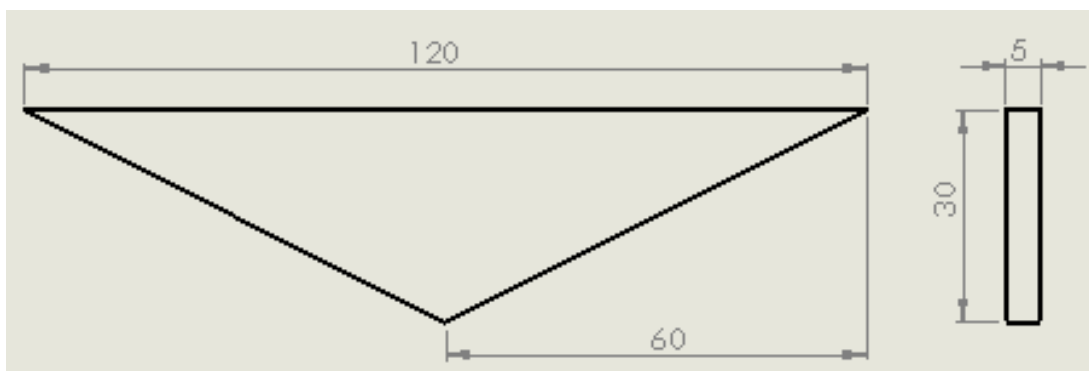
Dimensões dos triângulos impressos, dimensões em mm.
